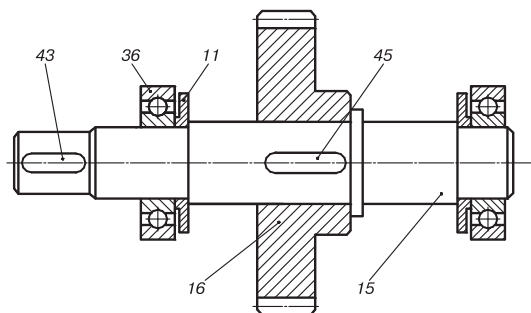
Вал тихоходный в конструктивном исполнении редуктора (см. рис. 5.3)
